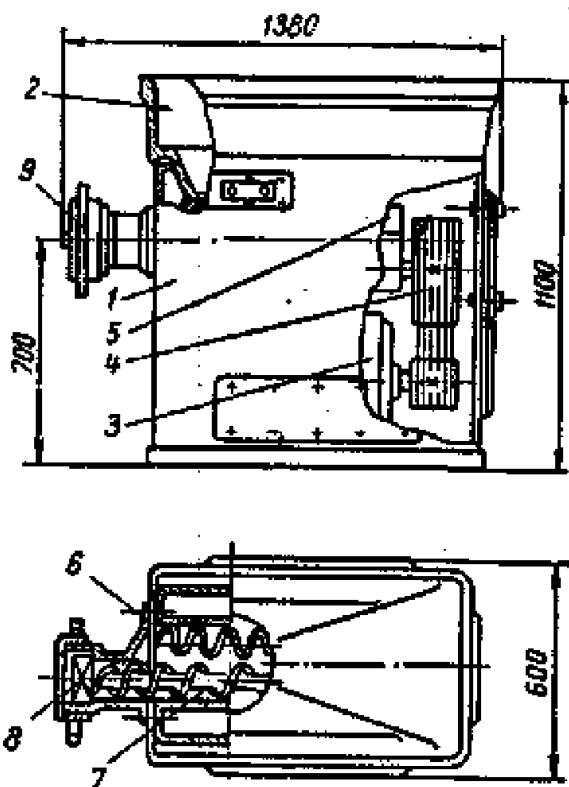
Вовчок МП-2-160: 1 – станина; 2 - завантажувальна чаша; 3 – електродвигун; 4 – клинопасова передача; 5 – редуктор; 6 – подаючий шнек; 7 – робочий шнек; 8 - ріжучий механізм; 9 – гайка.
